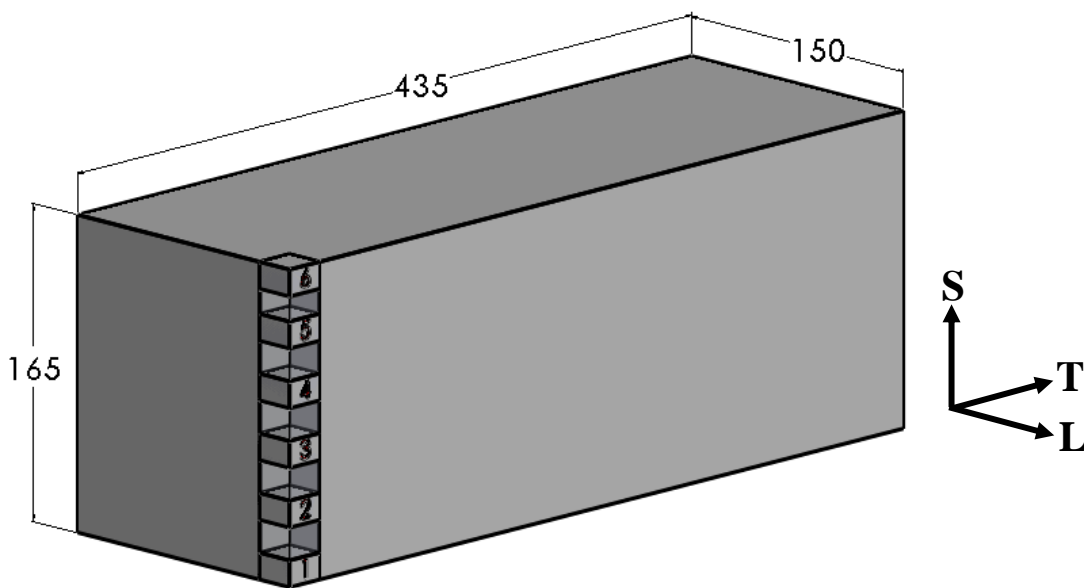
Bloco de Al 7050-T7451 investigado (dimensões em mm).
